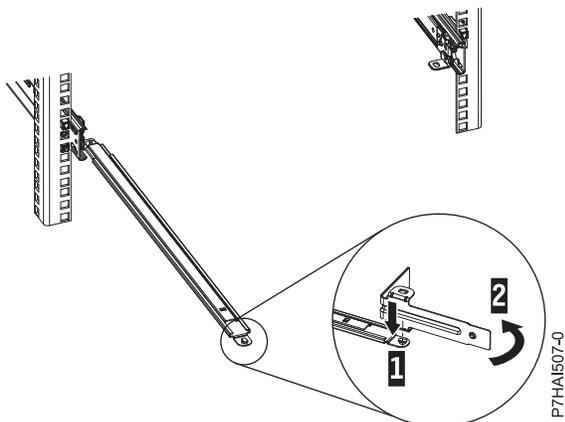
Suporte de paragem de gestão de cabos presa ao braço de suporte
